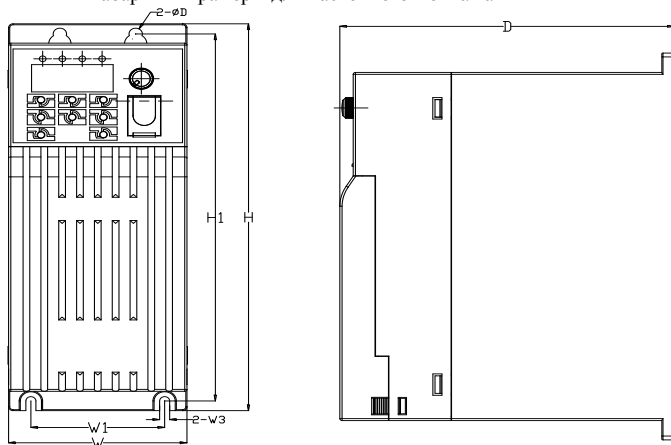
0.7~2.2кВт монтажный чертеж стен
